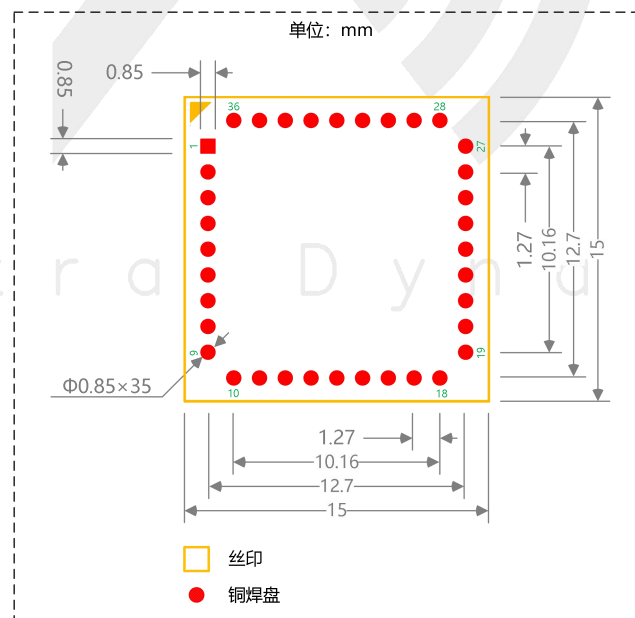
xmBLE-17H66B2-TI 推荐 PCB 封装尺寸
